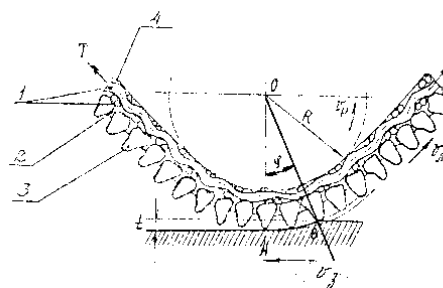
Схема ленточного шлифования: 1 — тканевая основа, 2 — связка, 3 — зерно, 4 — аппрет; φ — угол контакта, AB — длина дуги контакта, V_l — скорость ленты, V_z — скорость заготовки, R — радиус ролика
